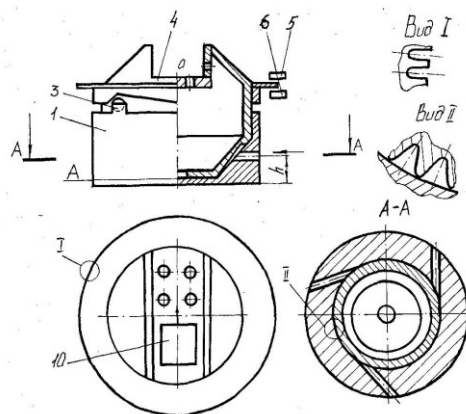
Устройство для бесконтактных взвешивания и сортировки штучных изделий по массе: 1 - корпус; 2 - дроссели для подачи сжатого воздуха; 3 - шаровая опора; 4 - промежуточная платформа - ротор; 5 - источник светового сигнала; 6 - фотозлемент; 7 - изделие.
